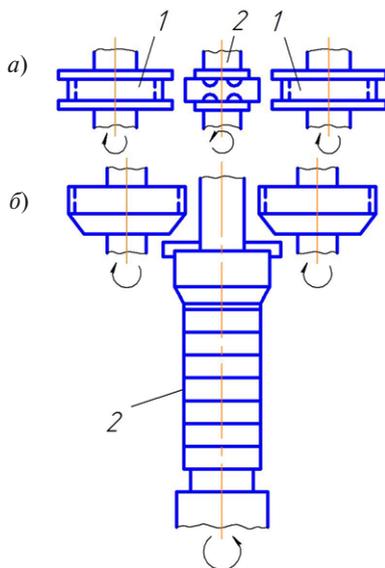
Схемы накатки: *а* – штучных заготовок; *б* – от прутка; 1 – деформирующий инструмент; 2 – заготовка
